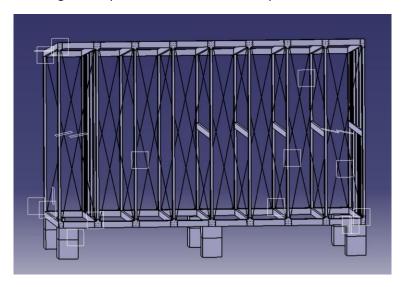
Imagen del modelo 3D sin travesaños Fuente: elaboración propia
